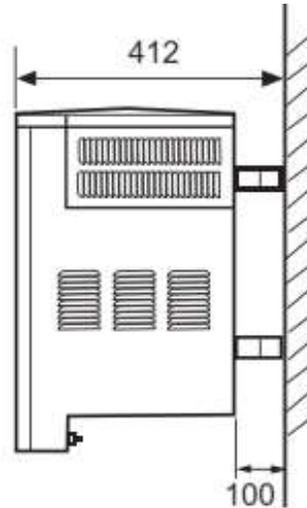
Dimensiones totales junto con los soportes de montaje en pared.
